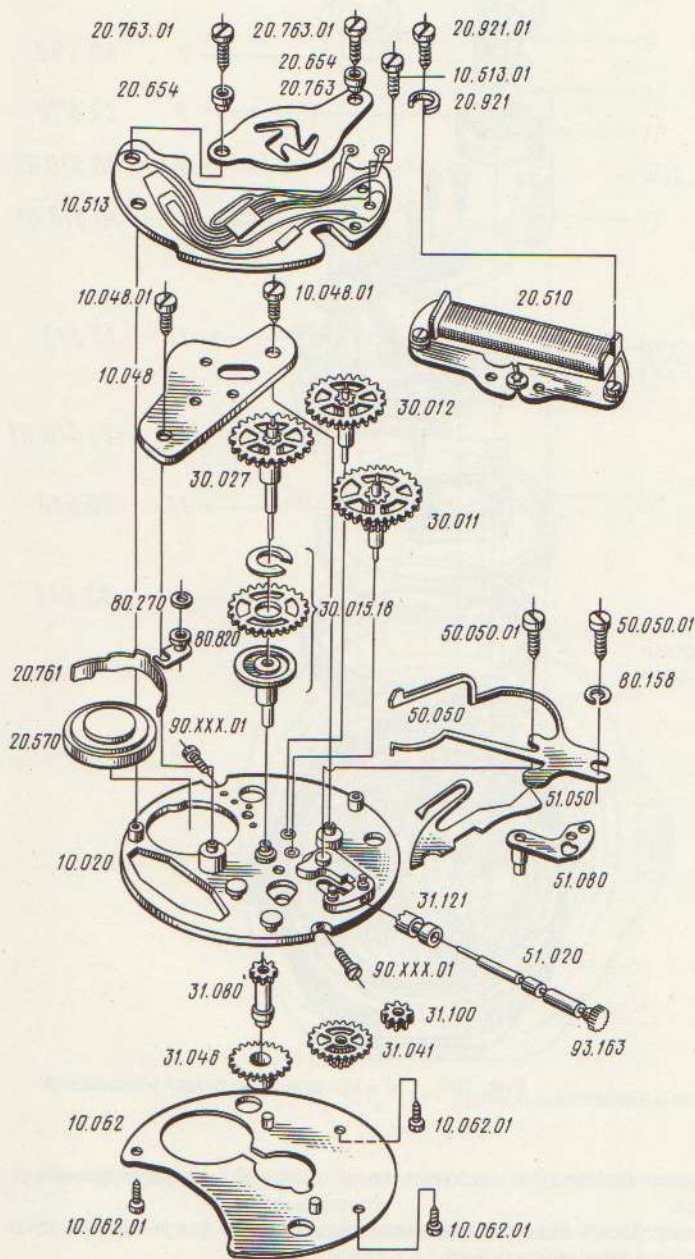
Детали и сборочные единицы механизма часов 3056А:
